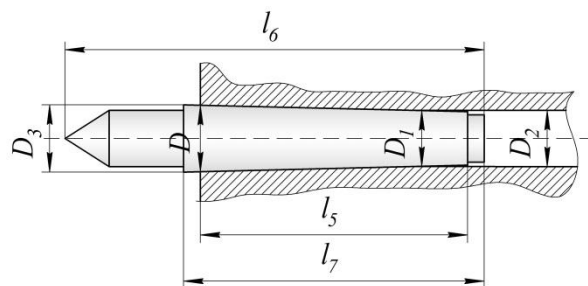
Эскиз конца пиноли задней бабки станка с упорным центром
